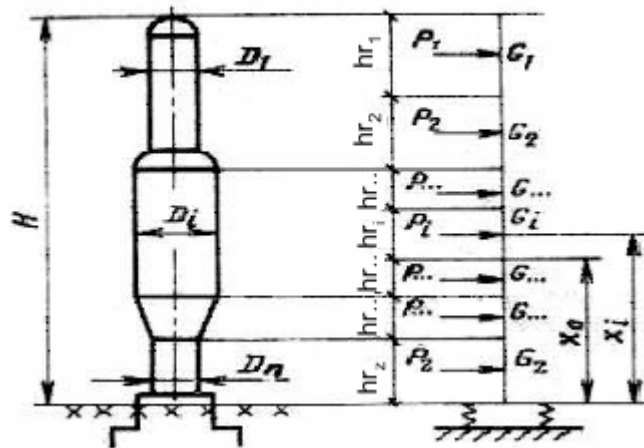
Расчетная схема аппарата колонного типа для определения ветровой нагрузки
